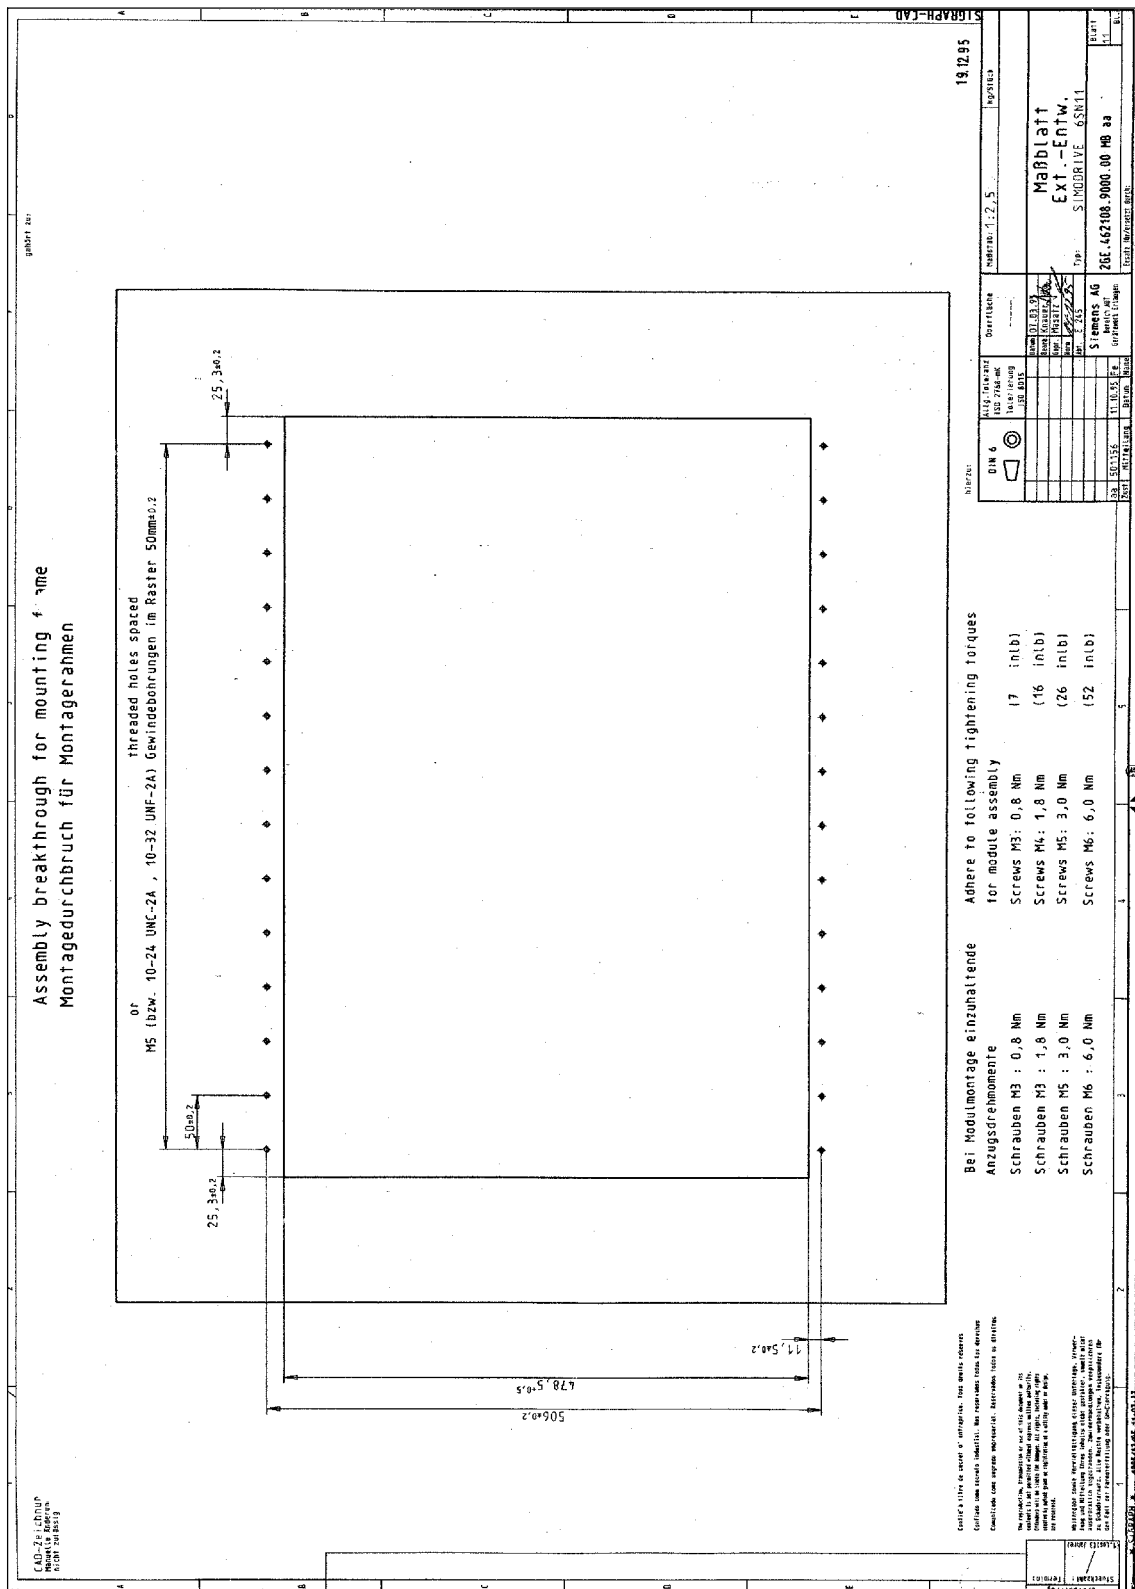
Refroidissement externe, découpe de montage pour châssis
